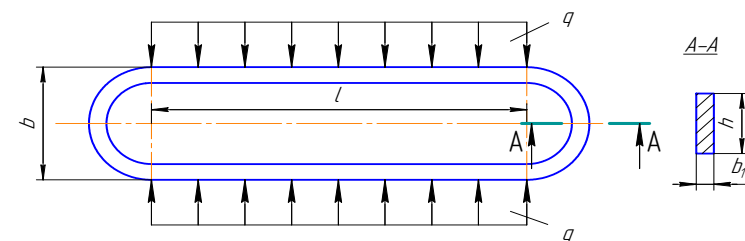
Розрахункова схема пружної шпонки з пустотілою частиною концентричною зовнішній формі
